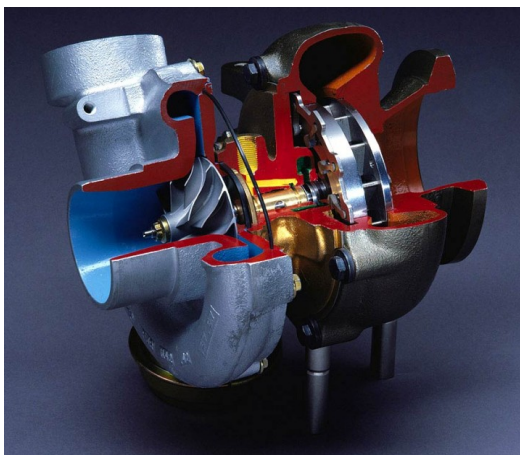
Imagen de Conjunto de un Turbocompresor
